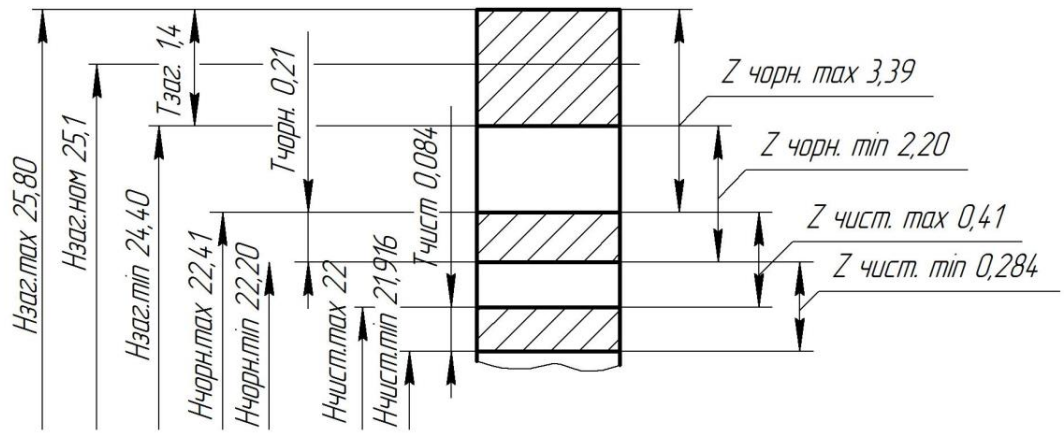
Схема розміщення припусків та допусків на обробку площини В
